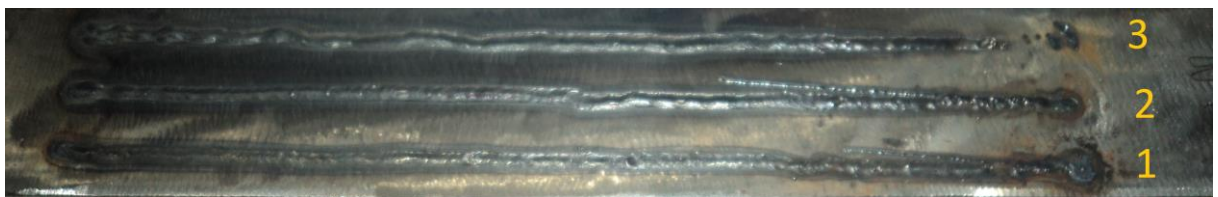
7 - Imagem dos três cordões de solda citados no parágrafo acima. A ordem de soldagem foi feita de acordo com a numeração da imagem.
